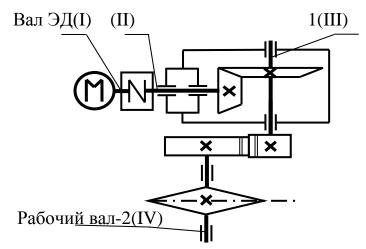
Образец схемы привода с открытой цилиндрической передачей
